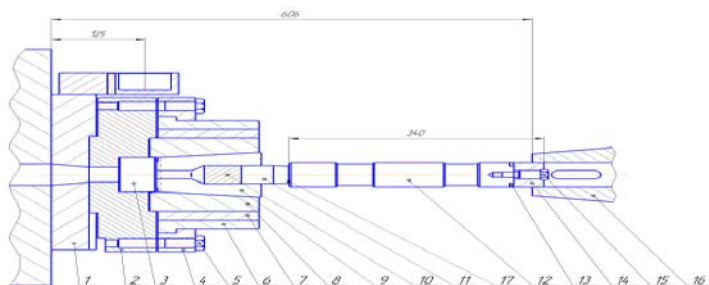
Схема штампа для СВГ биметаллических стержневых деталей
